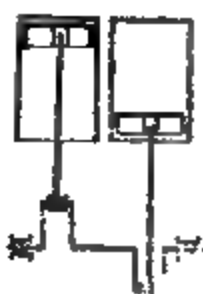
Parallel Zweicyl.-Maschine, einf. wirk., Kurbeln 180° versetzt.
